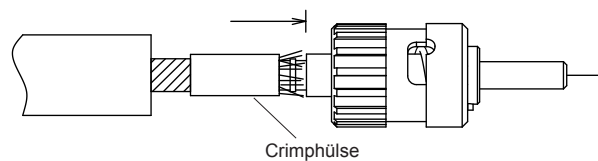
F-ST Steckverbinder mit Crimphülse und Knickschutztülle
